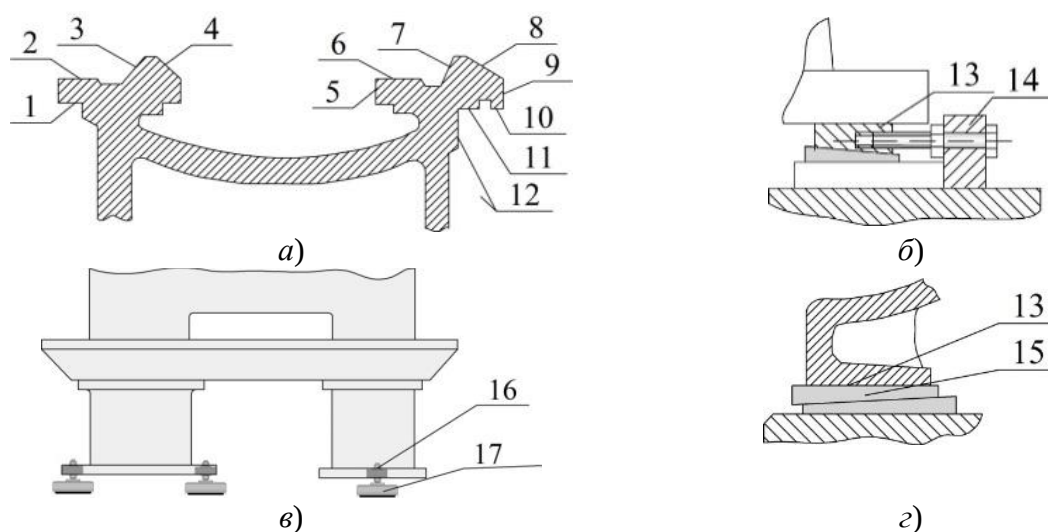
Схемы станины (а) токарного станка и ее установки с помощью: башмаков (б), домкратов (в), клиньев с регулировочными винтами (г): 1...12 – поверхности станины; 13 – подошва станины; 14 – башмак; 15 – клин; 16 – болт домкрата; 17 – опора
